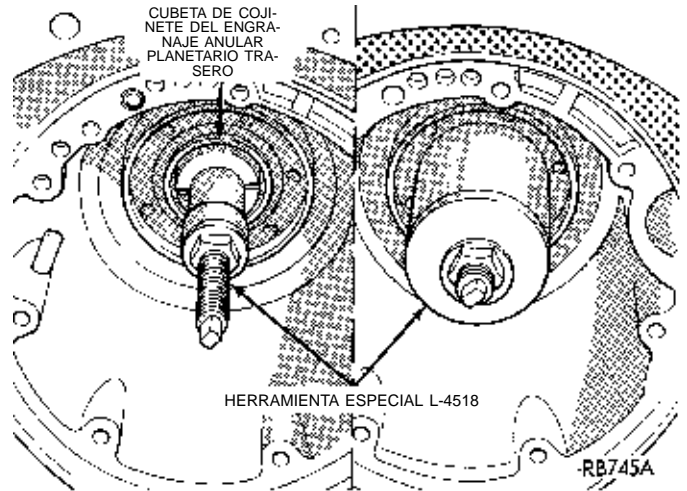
Desmontaje de la cubeta de cojinete del engranaje anular planetario trasero
